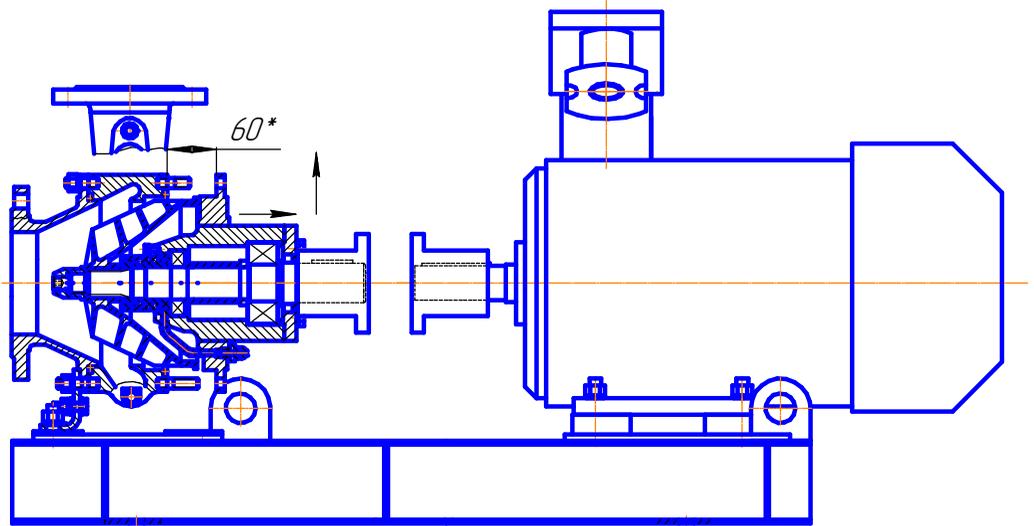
Устройство муфты МДП-2 и схема центровки валов
